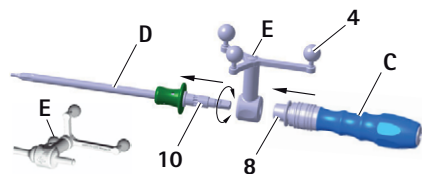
Монтаж звездчатого опорного блока (калибровка с помощью ICM 4) и ручки S⁴C (FW067R или FW165R) на метчике S⁴C
